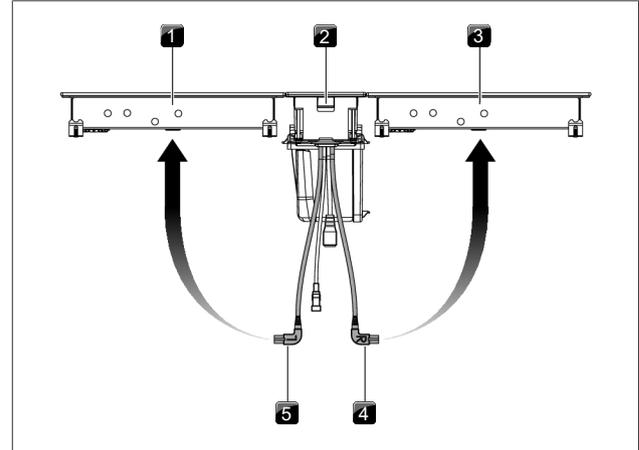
Steuerleitungen an die Kochfelder anschließen
